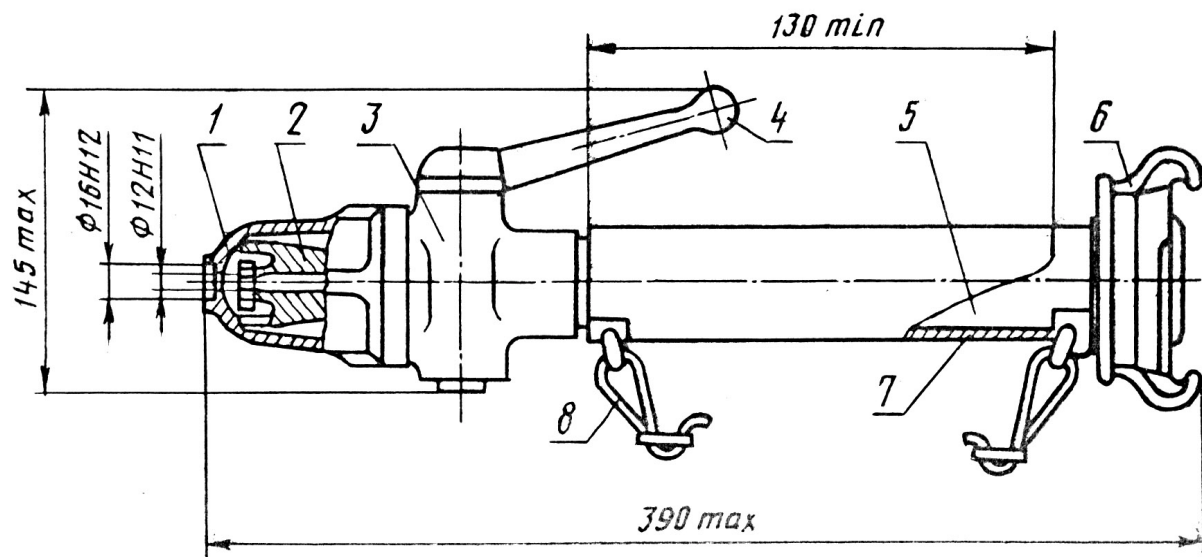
стакан, 2-вкладыш, 3-перекрывающее устройство, 4-ручка, 5-корпус ствола, 6-соединительная головка ГМН-50, 7-термоизолирующий чехол, 8-ремень.
